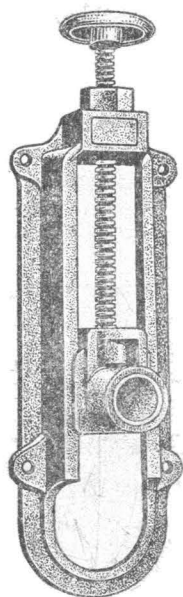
Вертикальное реечное натяжное приспособление для лент.
